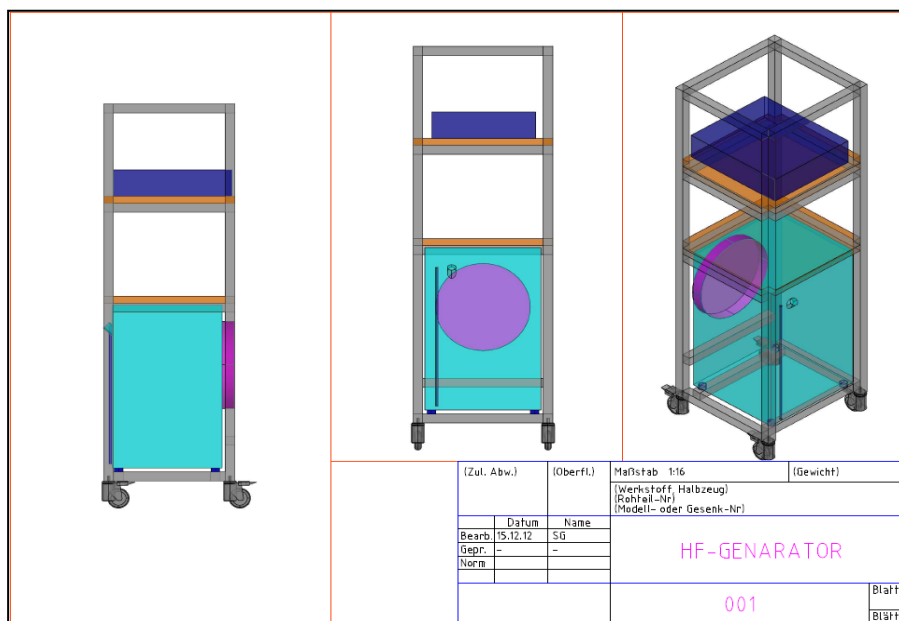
Modul - Rack für HF-Technik mit Rückkühler
